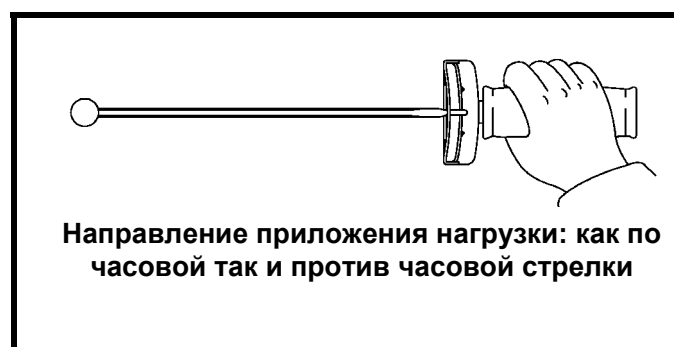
Правильный захват рукоятки динамометрического ключа
